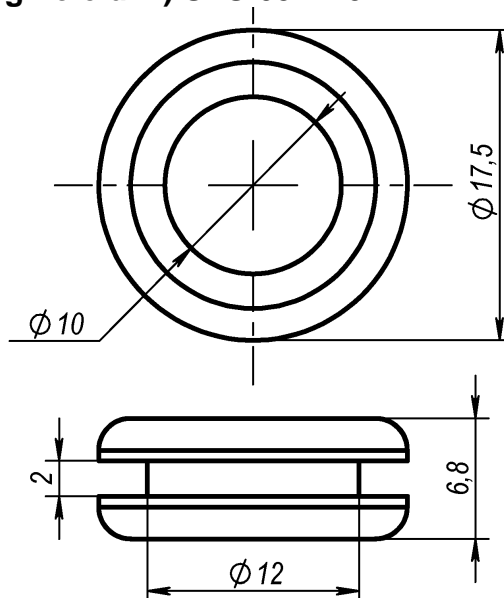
Кольцо GM-50 (mounting hole d12)
